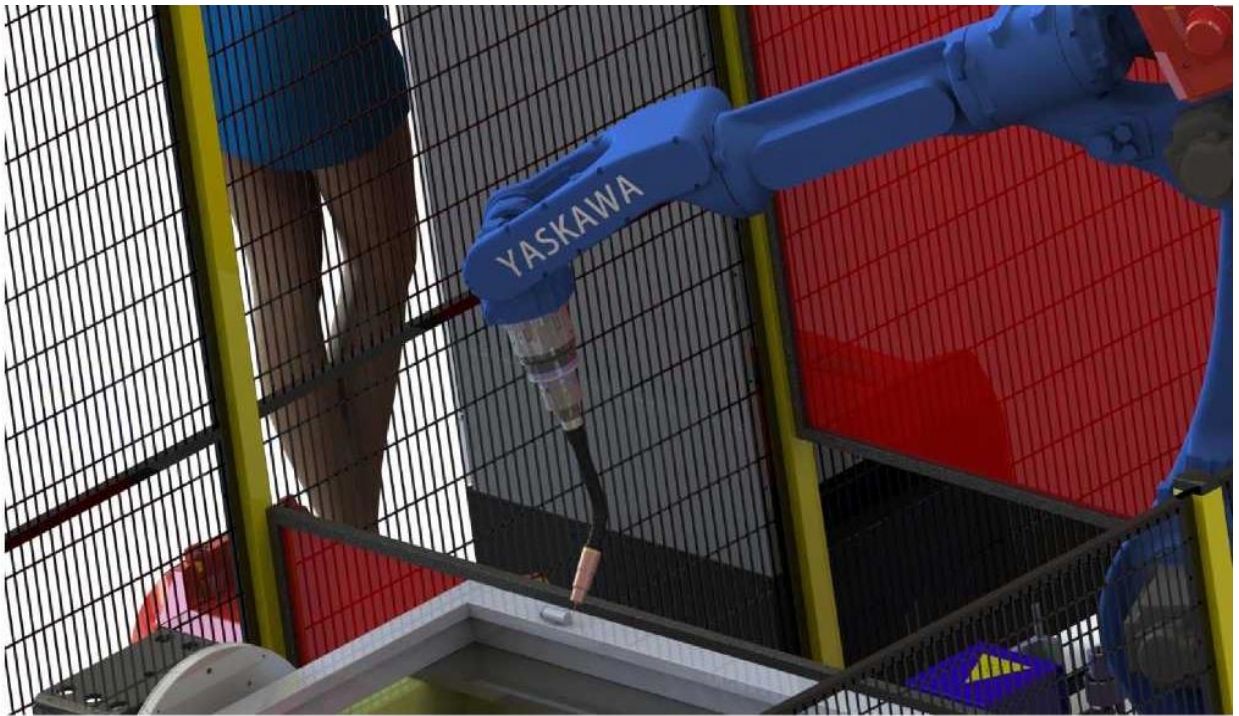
Схематичне зображення робочої зони роботизованого комплексу, зварювання дверної рами
